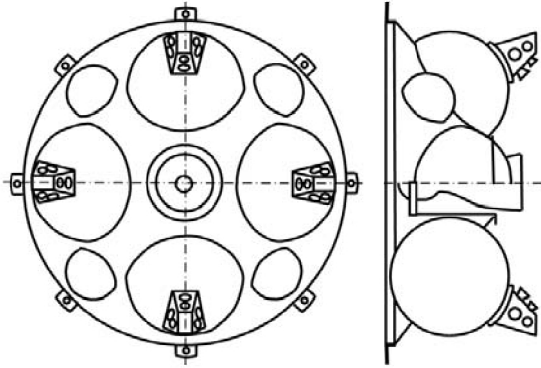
Компонировочная схема комплексной двигательной установки с передачей усилия на верхнюю часть приборно-агрегатного отсека
